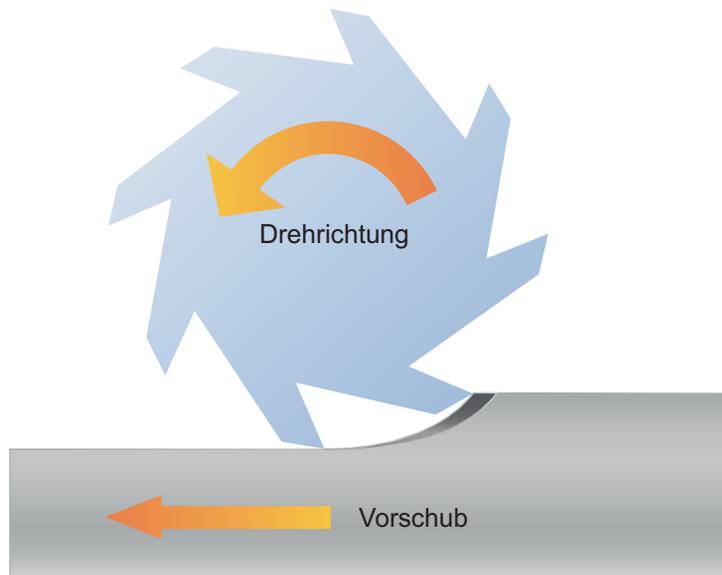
Beim Gegenlaufräsen wird das Werkstück in die Schneide hineingeschoben.
